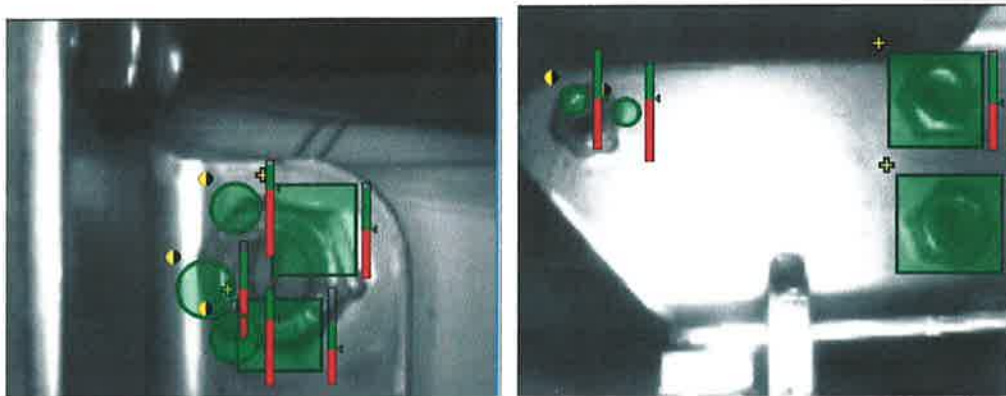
a) Configuración de sensores de inspección en la tuerca M14 de la pieza izquierda. b) Configuración de los sensores de inspección para tuercas M12 y M10 del Center Bracket izquierdo.
